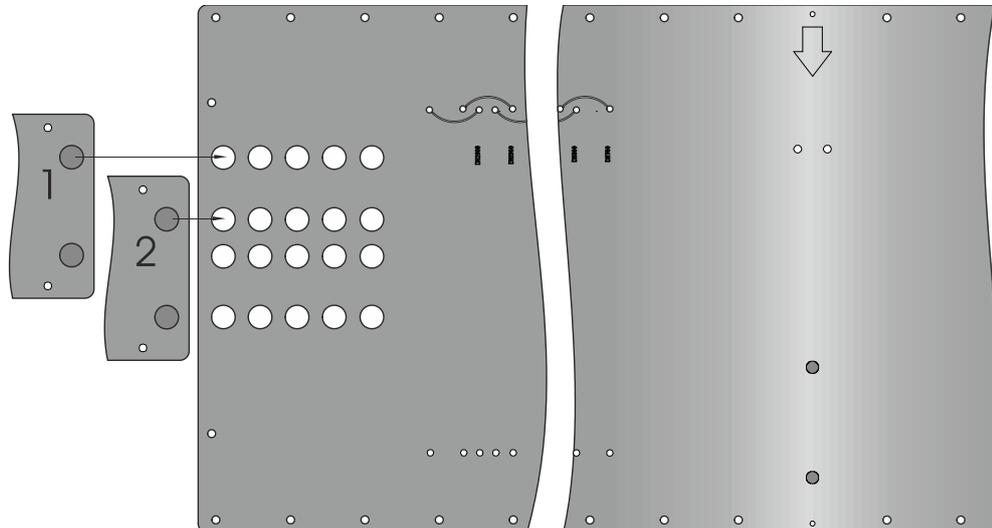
RMS 5 waagrecht montiert (vor dem Einbau)
